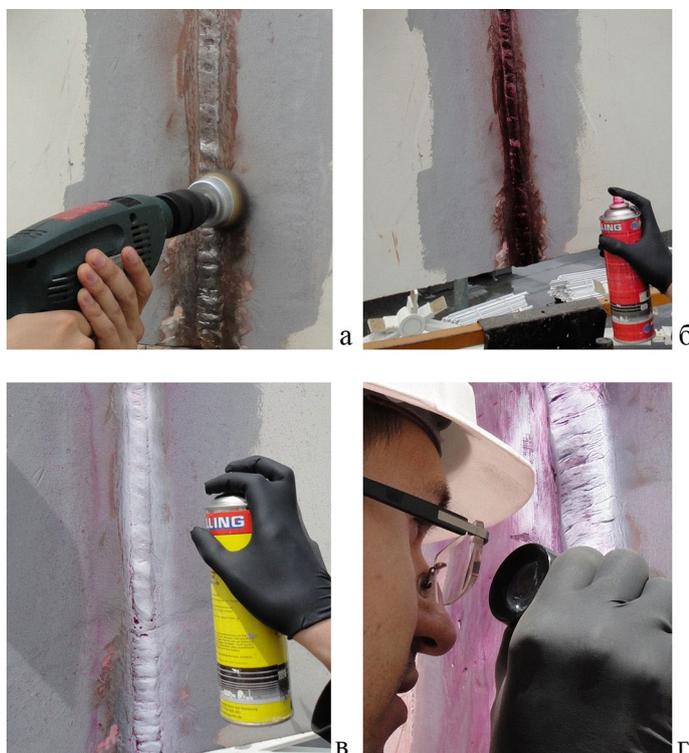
Капиллярный контроль: а) подготовка поверхности сварного соединения; б) нанесение индикаторного пенетранта; в) нанесение проявителя; г) визуальный контроль соединения
